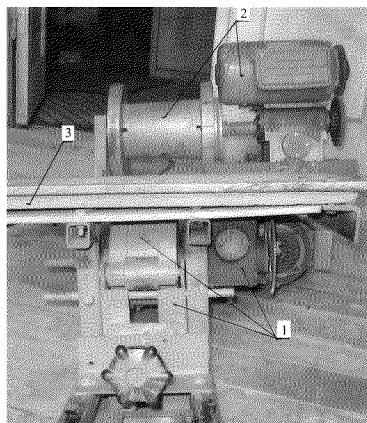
Общий вид модернизированного узла опытной установки для получения непрерывнолитых профилей в вакууме:
